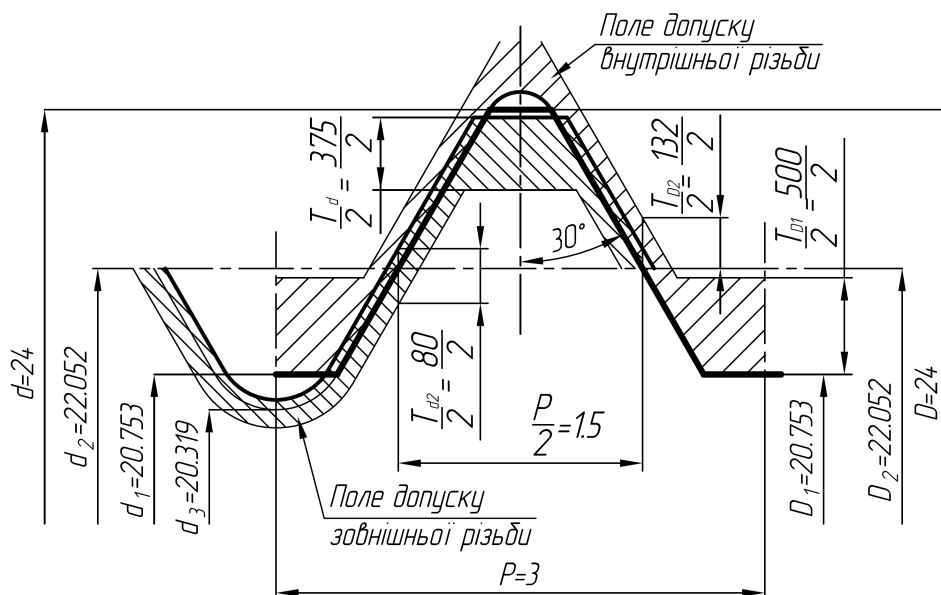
Схема розташування полів допусків різьбового з'єднання M24-3H6H/2m
